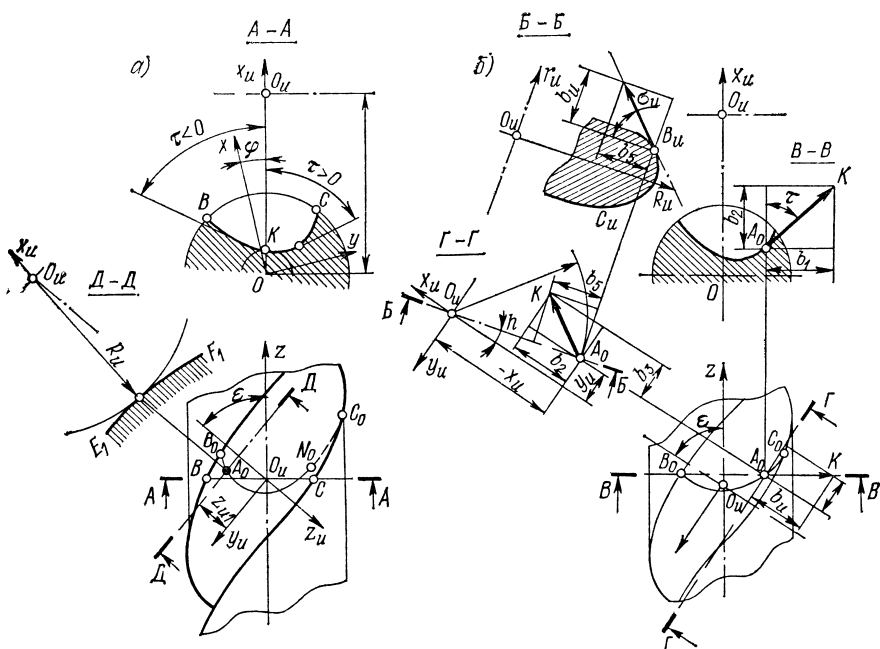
Схемы взаимного расположения обрабатываемой заготовки и производящего инструмента
